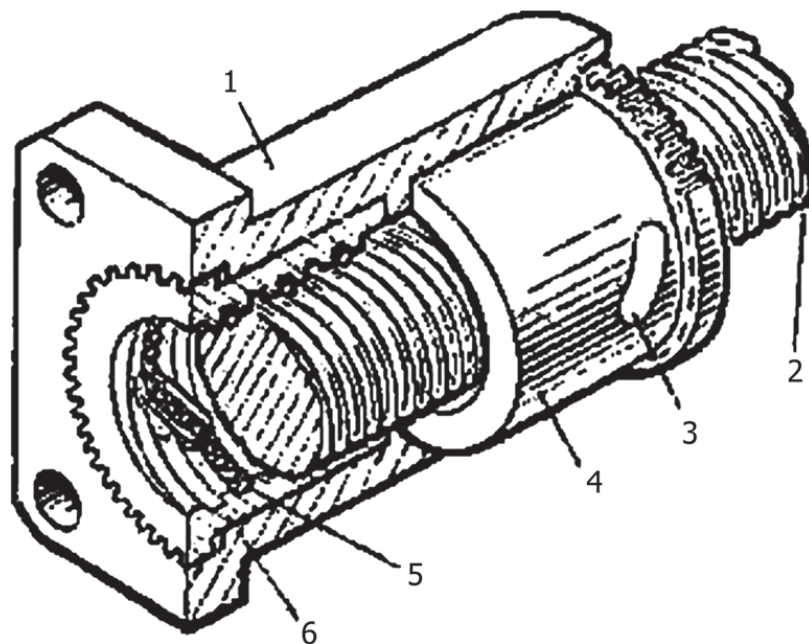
Конструкція кулькової гвинтової пари з подвійною гайкою та зубчастими вінцями для регулювання попереднього натягу
